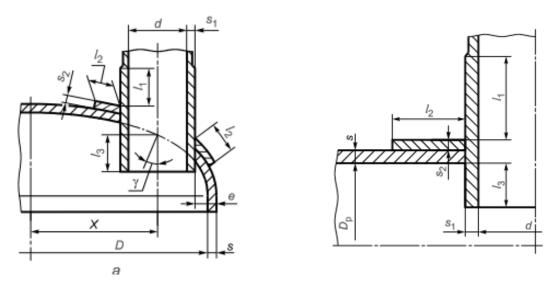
Схема расположения штуцеров и укрепления отверстий
